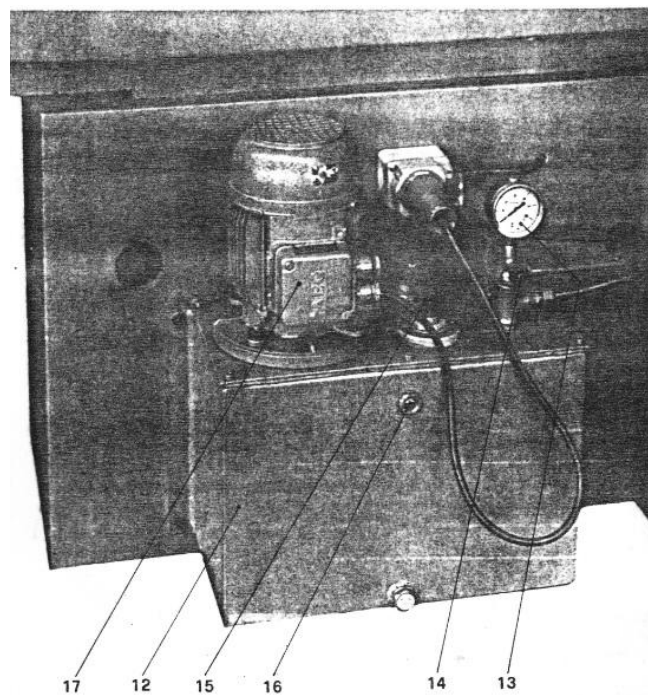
UNIDAD HIDRÁULICA DE MÁQUINA
